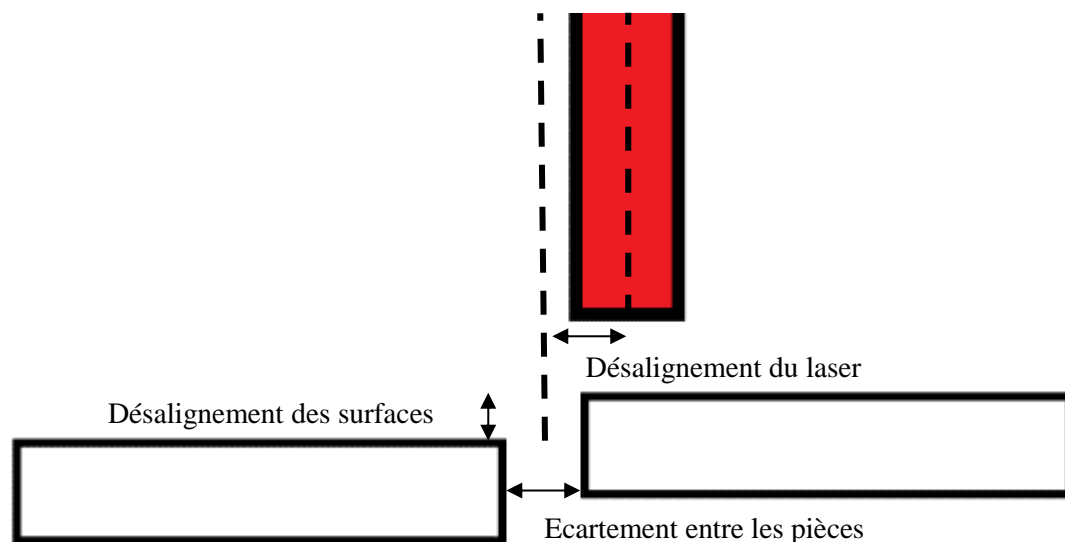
Défauts de positionnement pour le soudage bout à bout
